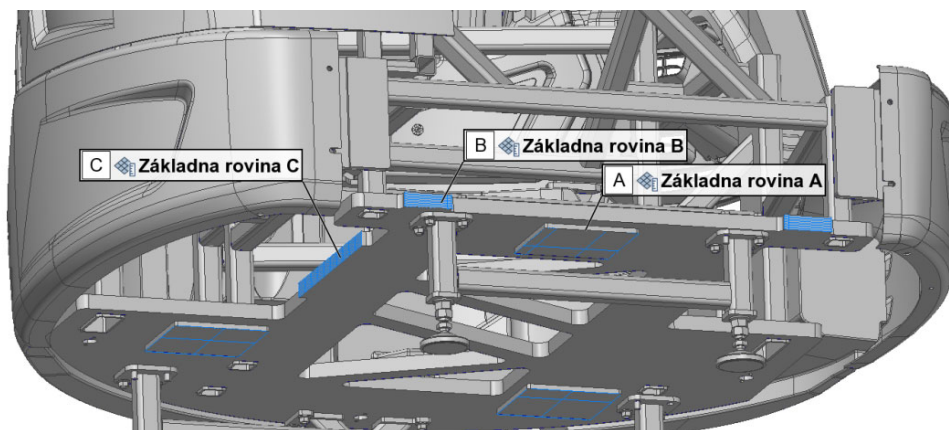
Výsledné zarovnání dvou mraček bodů
